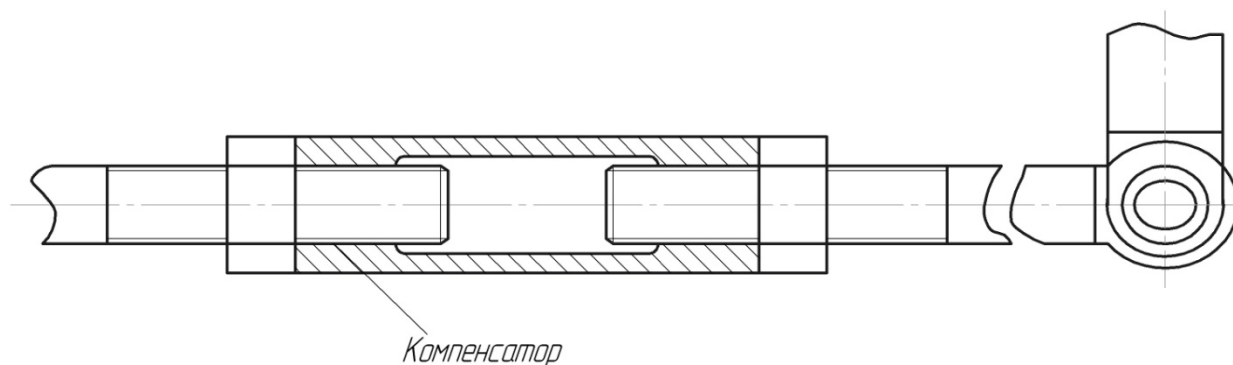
Способ регулирования зазора (натяга) между шарнирами с помощью гайки с правой и левой резьбой
